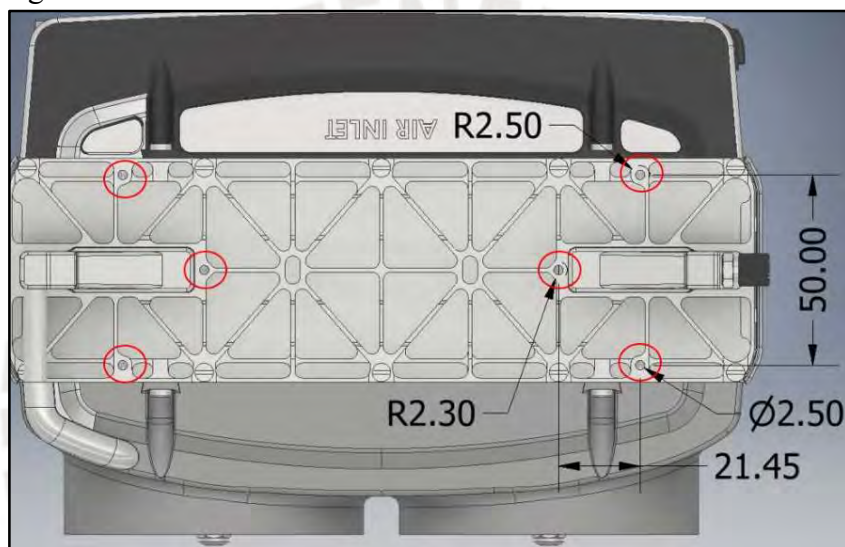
Vista de planta de módulo IE-SOAR 800 W. Fuente: Elaboración propia.
